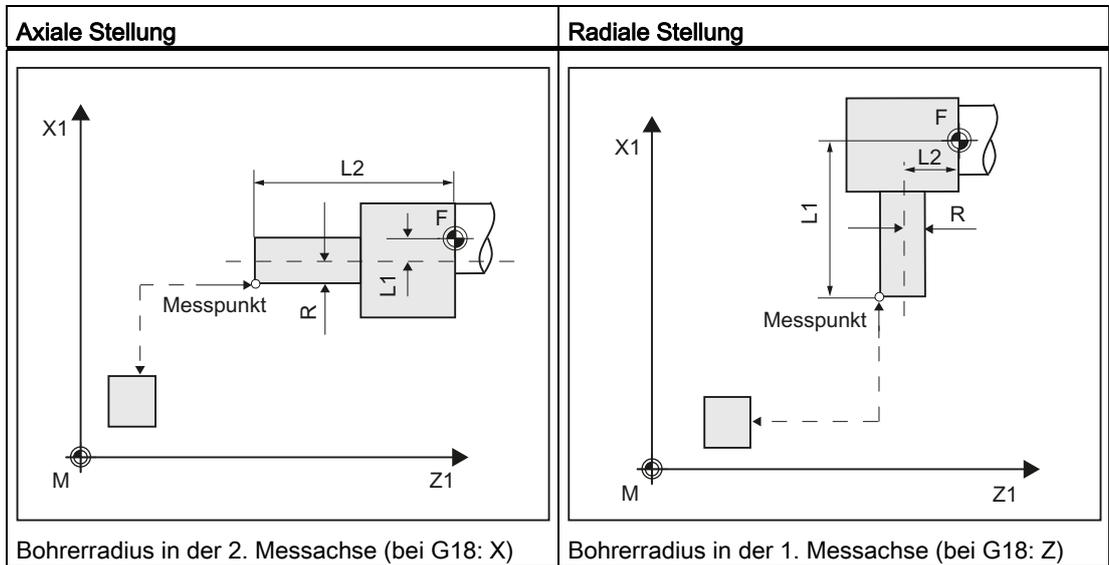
Messen: Bohrer (CYCLE982), Beispiel Werkzeuglage: ↓ radiale Stellung
